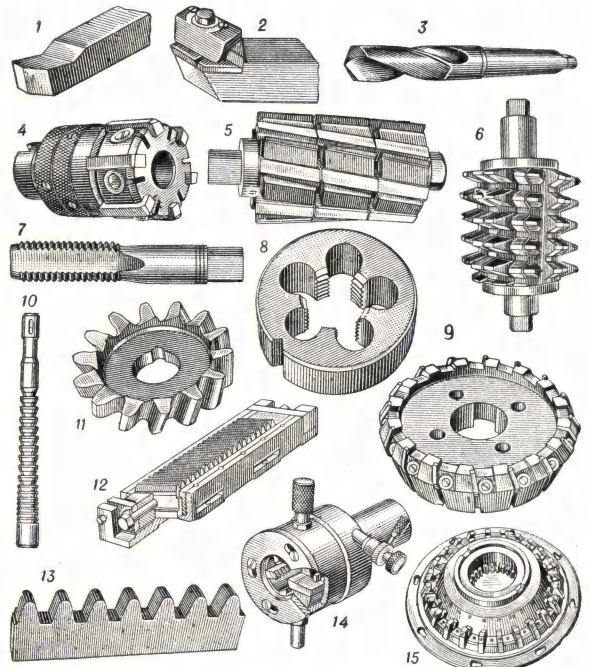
Типы металлоорежущих инструментов: 1 — проходной резец; 2 — резец с пластиной твёрдого сплава; 3 — спиральное сверло; 4 — развёртка с твёрдосплавными лезвиями; 5 — цилиндр. фрезы с твёрдосплавными лезвиями; 6 — червячная фреза; 7 — метчик; 8 — плашки; 9 — торцевая фреза с вставными зубьями; 10 — протяжки для отверстий; 11 — долбяк; 12 — шевер-рейка; 13 — зуборезная гребёнка; 14 — резьбо-нарезная головка; 15 — фасонная зубодолбежная головка.
